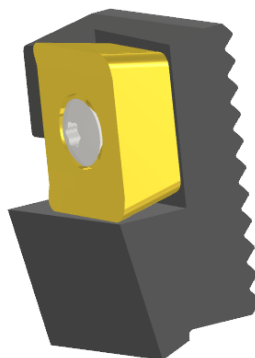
Зовнішній вигляд касети фрези дискової збірної для оброблення пазів
